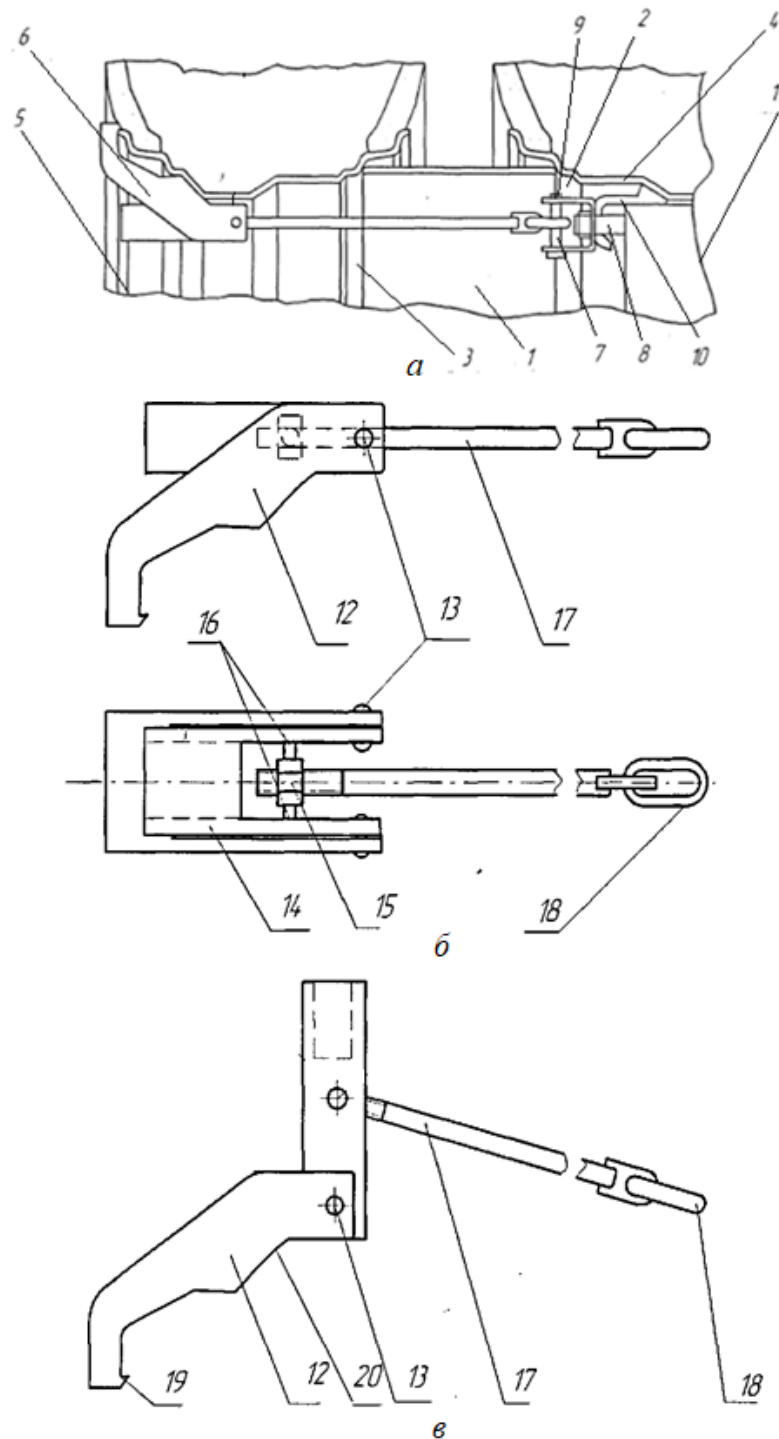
Пристрій для здвоєння коліс трактора ХТЗ-150К:
